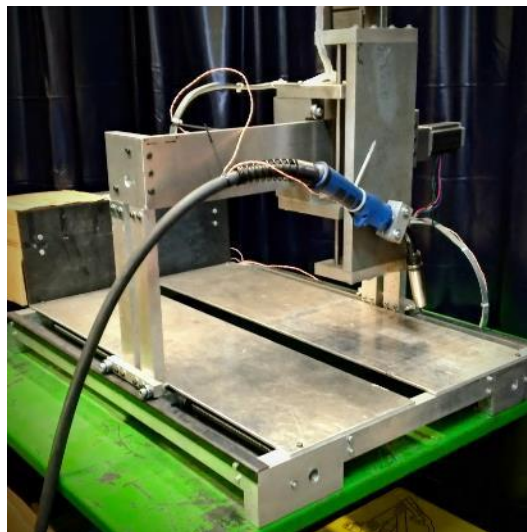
Equipamento CNC com adaptação da tocha de soldadura
